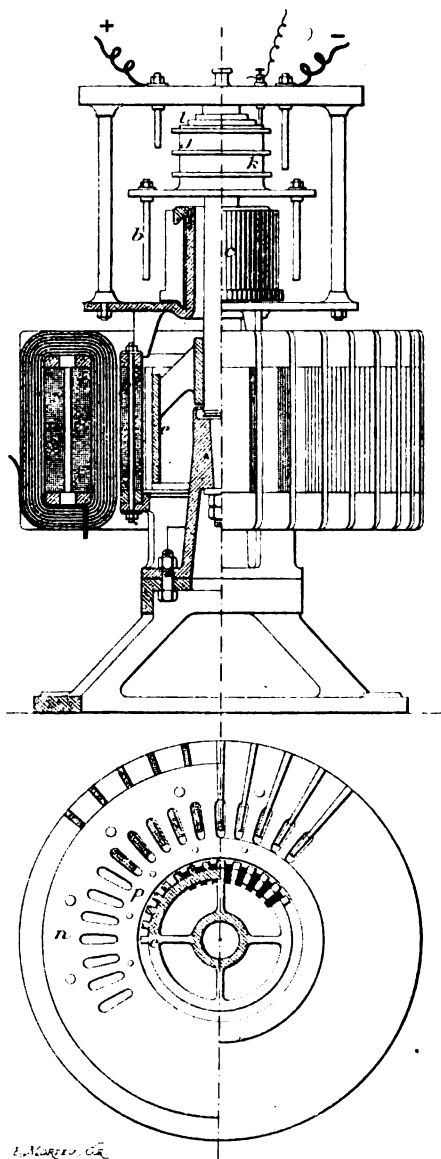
Élévation et coupe transversale. — Plan et coupe horizontale.
